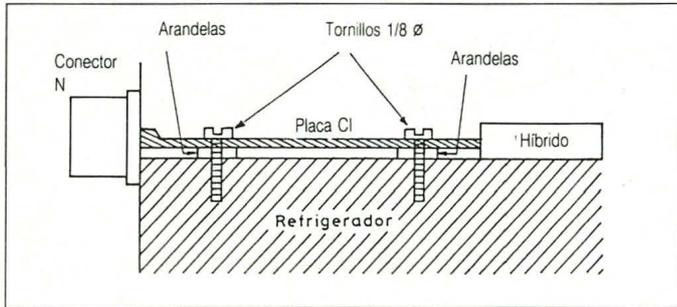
Detalle del montaje de la placa de CI sobre el refrigerador.
